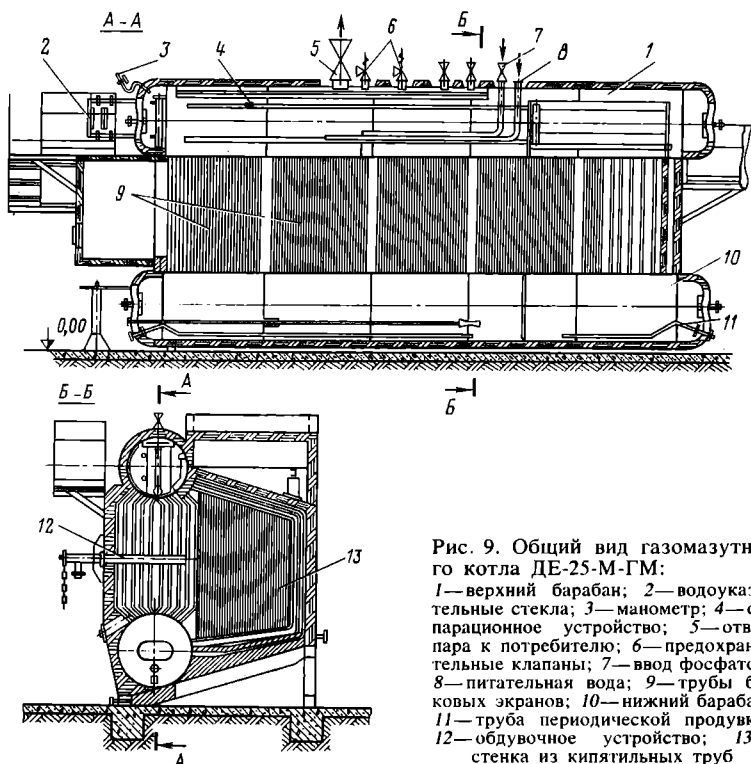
Общий вид газомазутного котла ДЕ-25-М-ГМ:
